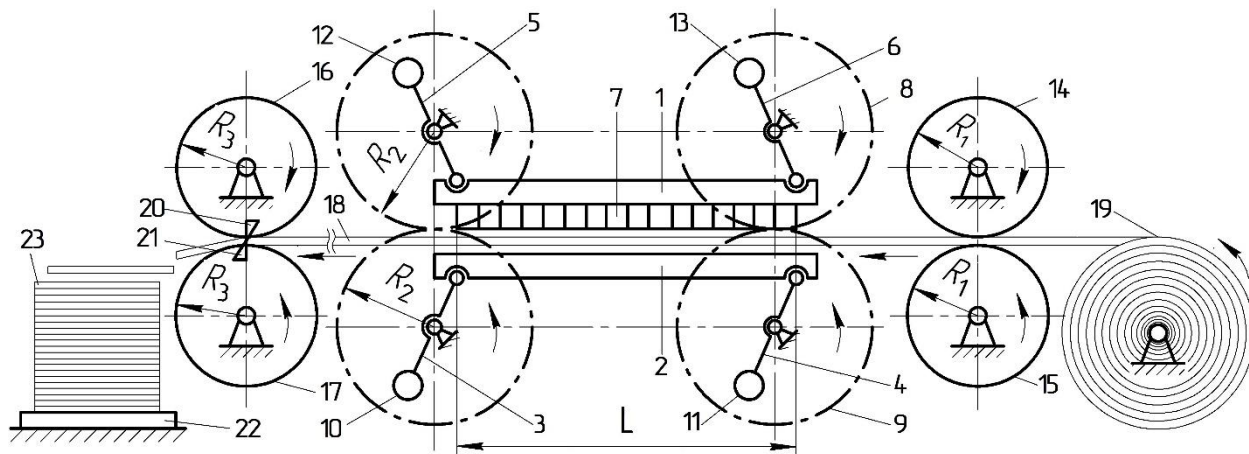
Графічна схема рулонного висікального пресу із кривошипними механізмами, 1 – формна плита; 2 – допоміжна плита; 3, 4, 5, 6 – кривошипи; 7 – штанцювальна форма; 8, 9 – зубчасті колеса; 10, 11, 12, 13 – противаги; 14, 15, 16, 17 – валики; 18 – стрічка палітурного матеріалу; 19 – рулон палітурного матеріалу; 20 – ніж; 21 – контрніж; 22 – палети; 23 – аркуші палітурного матеріалу.
